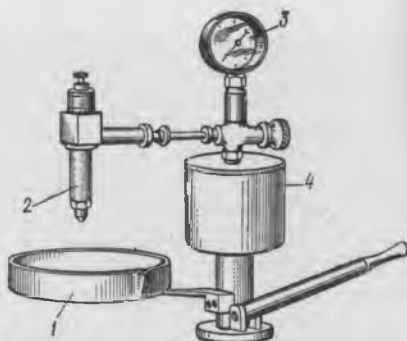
Установка для проверки распыления форсунок и регулировки давления открытия иглы:
